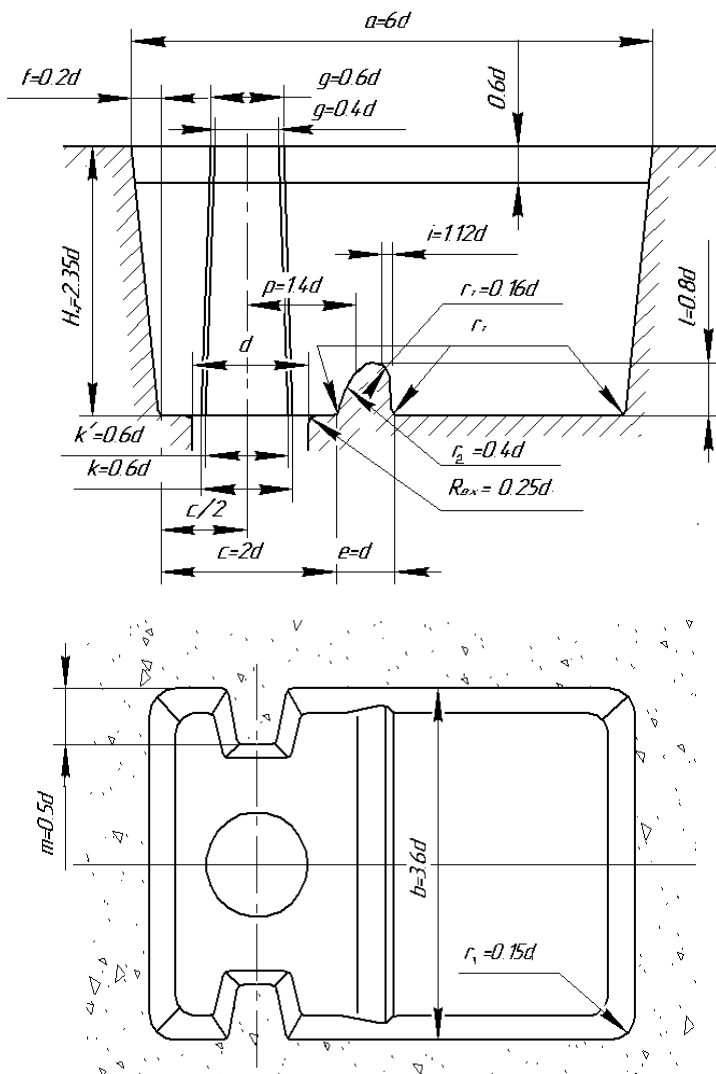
Эскиз формованной литниковой чаши с порогом, обеспечивающей расход металла до 10 кг/с
